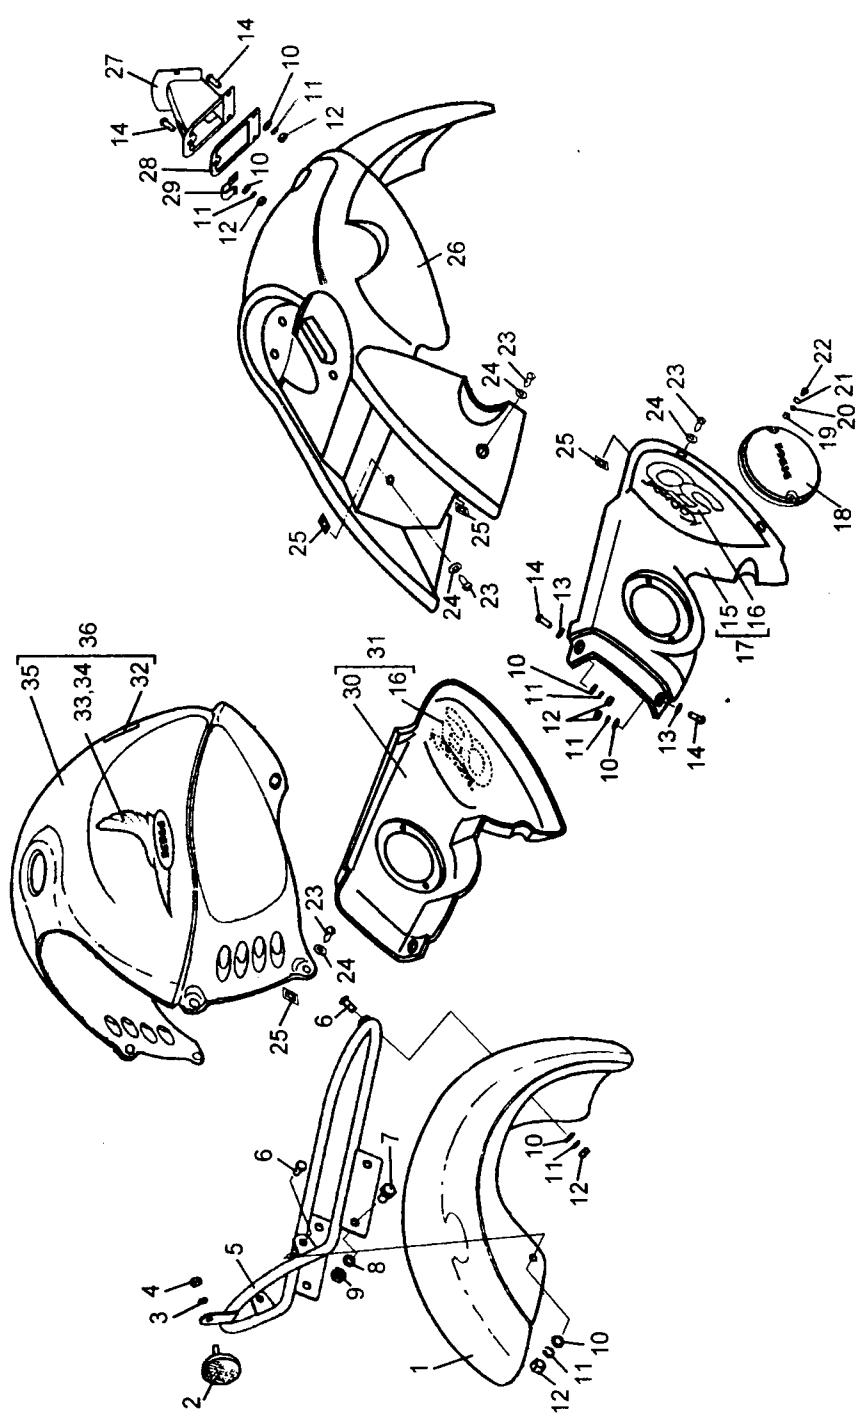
Щитки колес, кожух щитка заднего, накладки боковые
